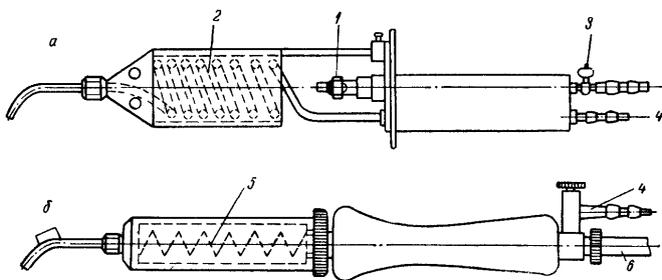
Схемы сварочных горелок:
